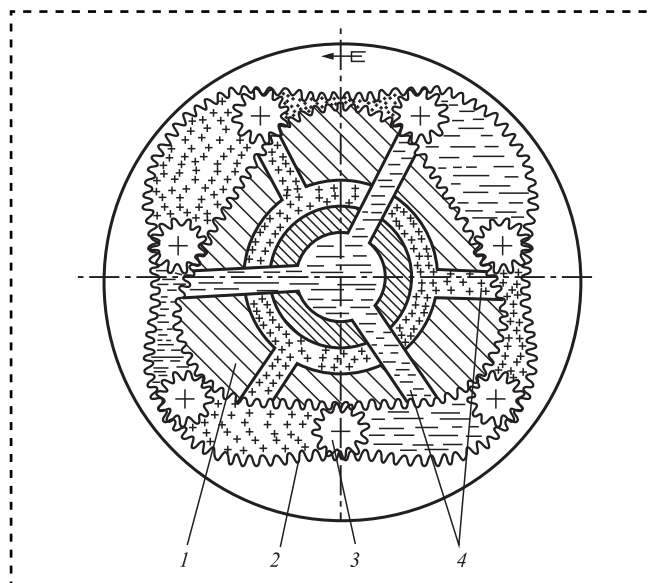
Объемный роторный двигатель схемы 4-3 [5]:
